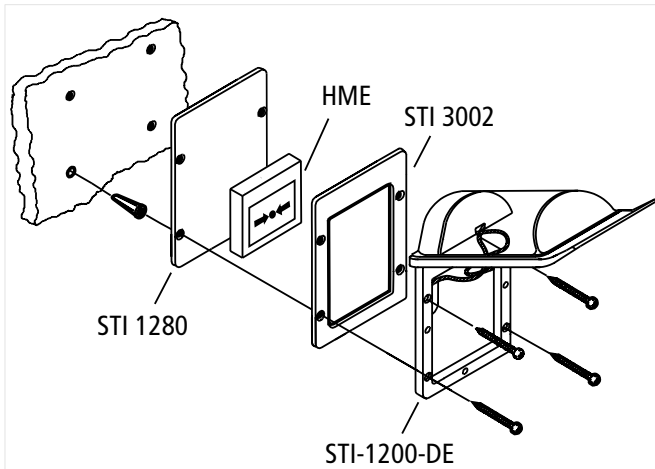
Montage Schutzhaube STI-1200-DE Kabeleinführung Unterputz
